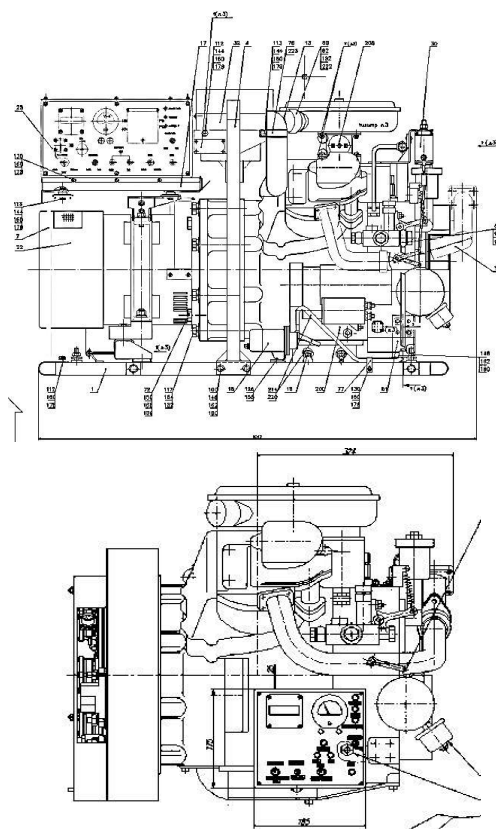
Габаритные размеры серийного агрегата (а) и опытного образца (б)
